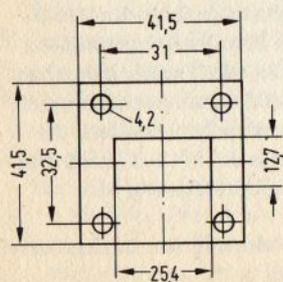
Flansch-Abmessungen für den Hohlleiter WG 16. (WR 90, R 100),
